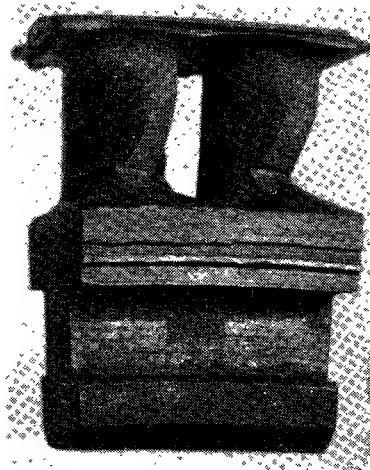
Абразивный износ пакета лопаток регуливающей ступени
